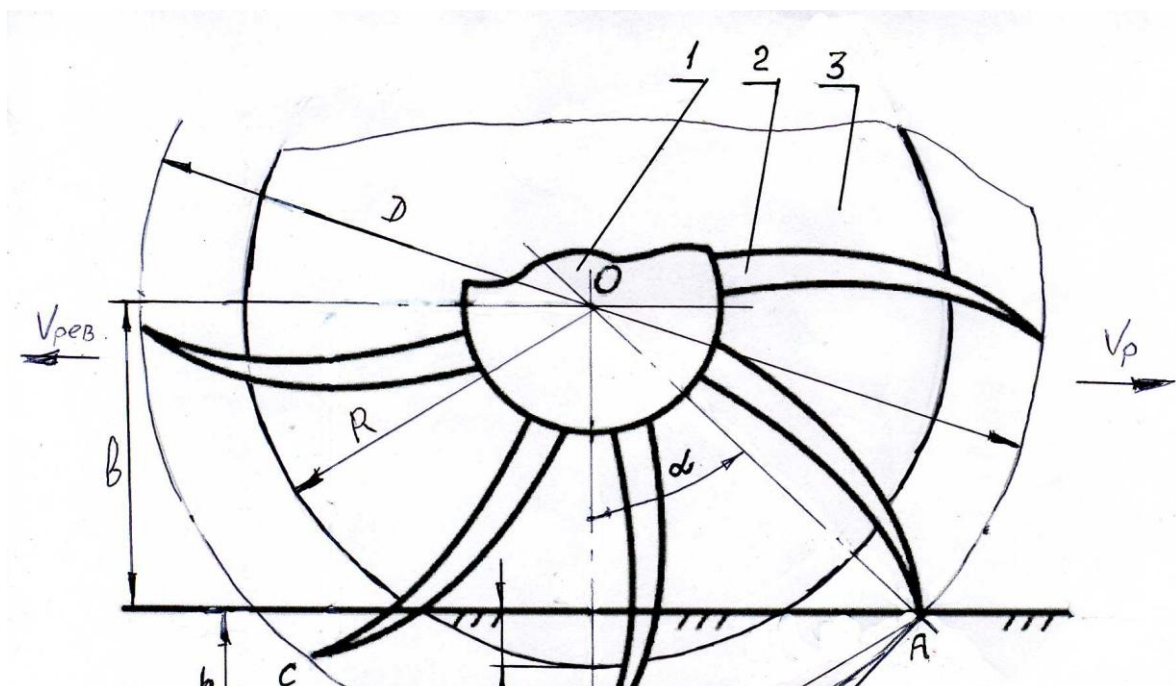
Розрахункова схема ротаційного зубового диска :
